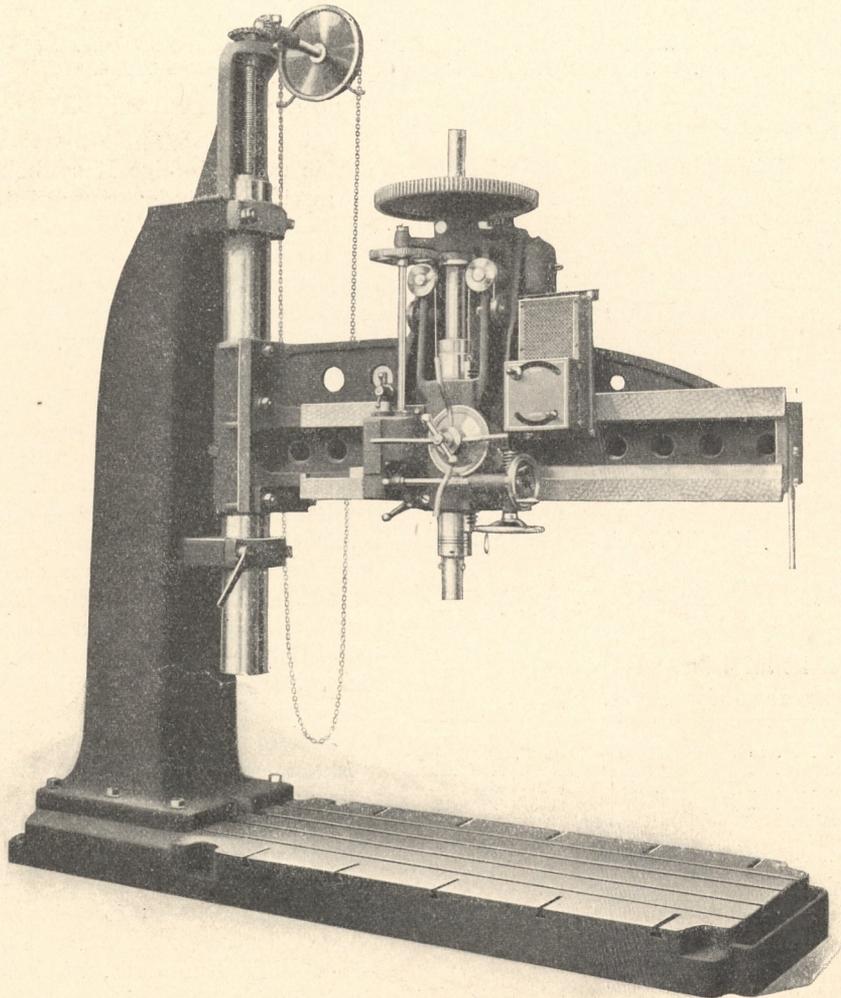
Schnellauf-Radialbohrmaschine. 80 mm Spindeldurchmesser, 2000 mm Ausladung.
